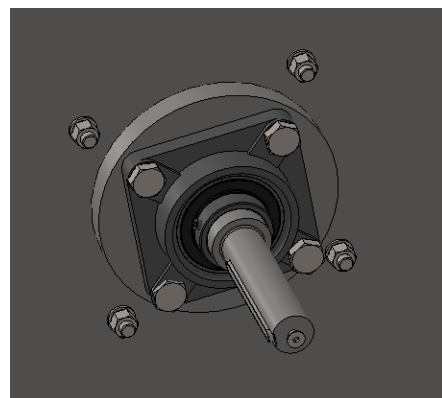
Vista inferior assemblatge unió rodaments amb l'hèlice
